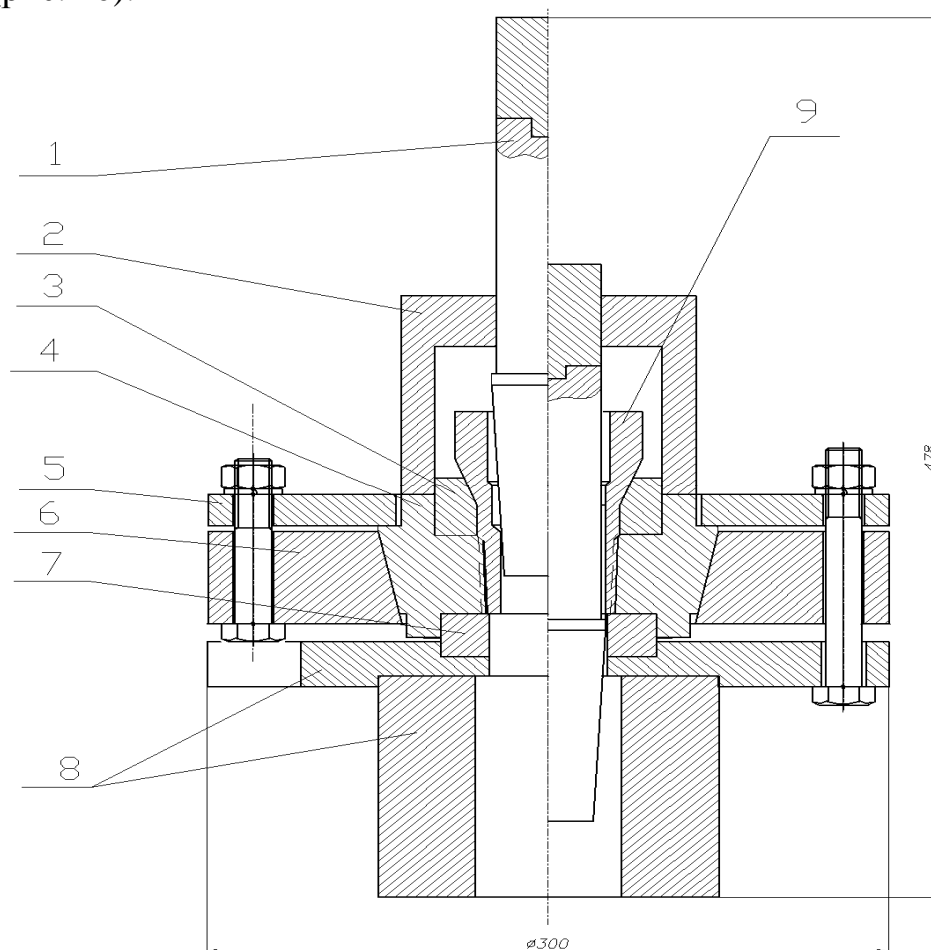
Оснастка для штамповки наружной резьбы на ниппельной части переводника с использованием цельной (и разъемной) резьбовой матрицы.
